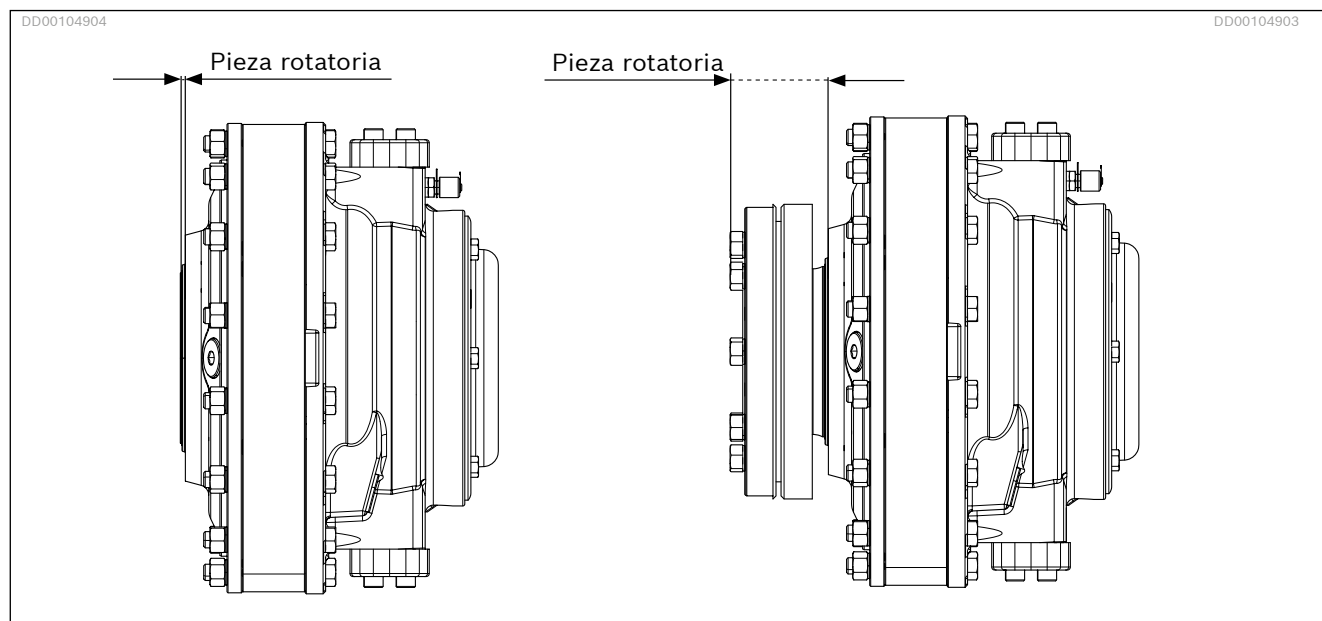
Pieza rotatoria, motor de estrías y motor de acoplamiento
